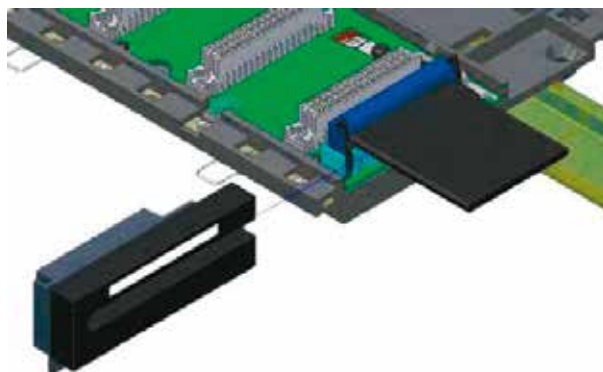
Установка защитного кожуха плоских кабелей
